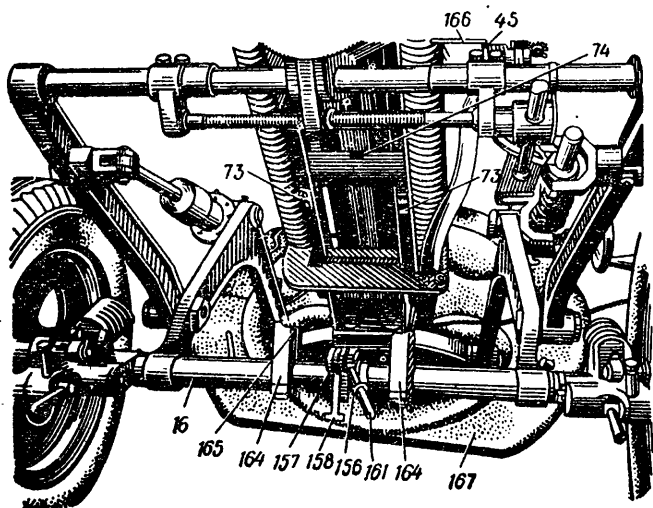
Приспособление старой конструкции для крепления качающейся части миномета по-походному (вид спереди, качающаяся часть приведена в среднее положение и снята с походного крепления):
